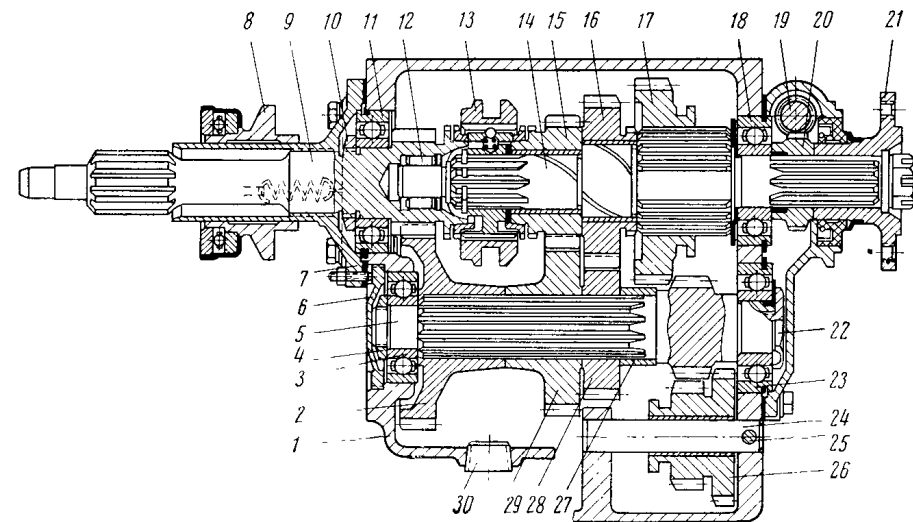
Коробка передач автомобиля УАЗ-451М:
